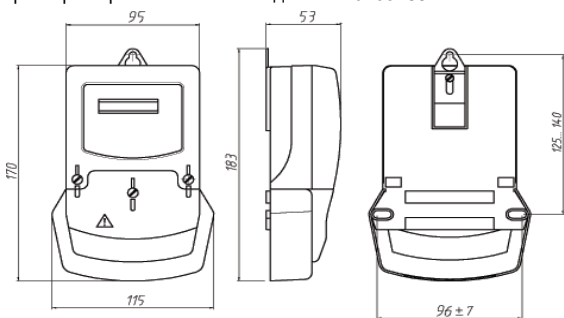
Загальний вигляд лічильника ЦЭ6807Б-У в корпусі ШБ
